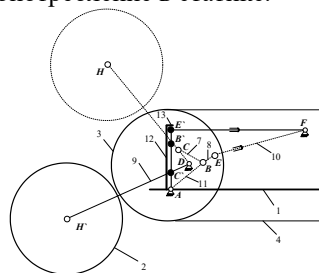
Кинематическая схема рычажного привода с системой упоров: 1 — платформа; 2 — колесо; 7 — поворотный рычаг (AB); 8 — шатун (BC); 9 — колесный рычаг; 10 — привод; 11 — направляющее коромысло; 12, 13 — механические упоры
